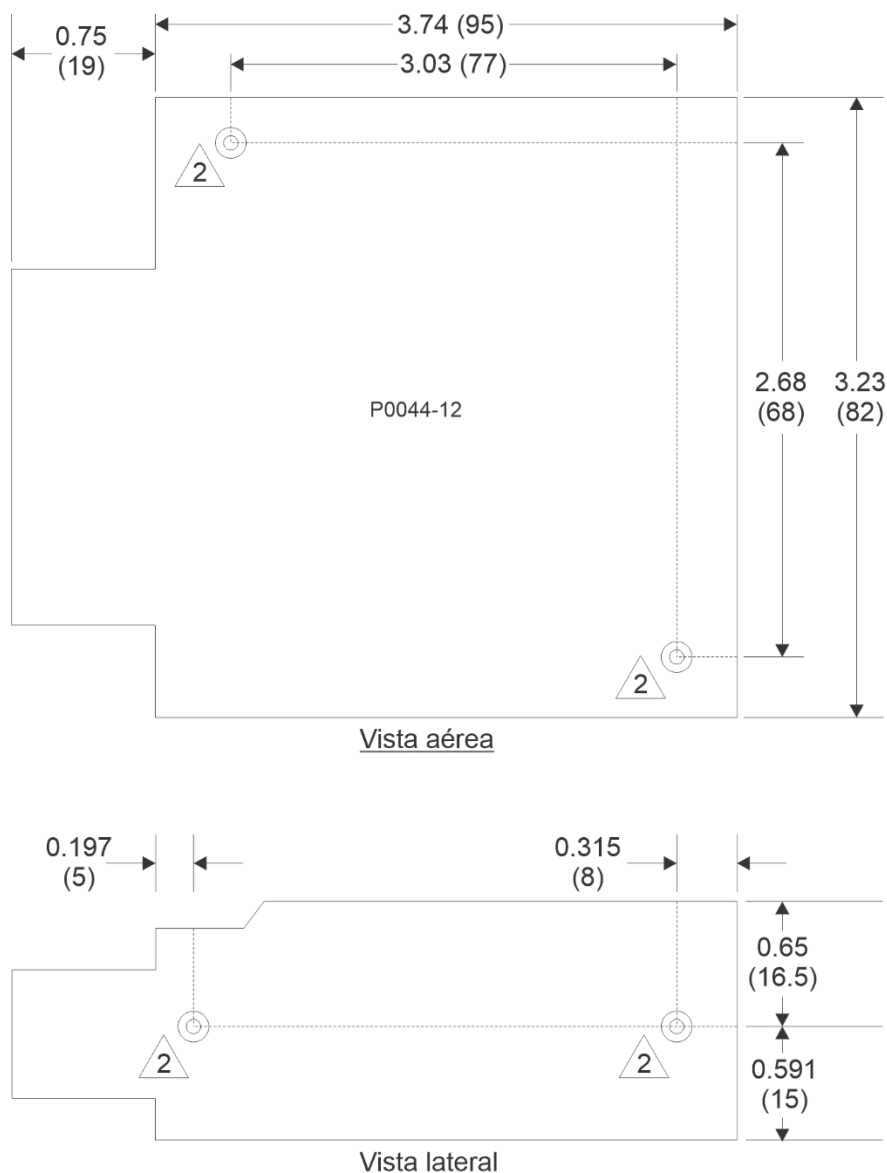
Dimensiones del riel de montaje del conmutador Ethernet
